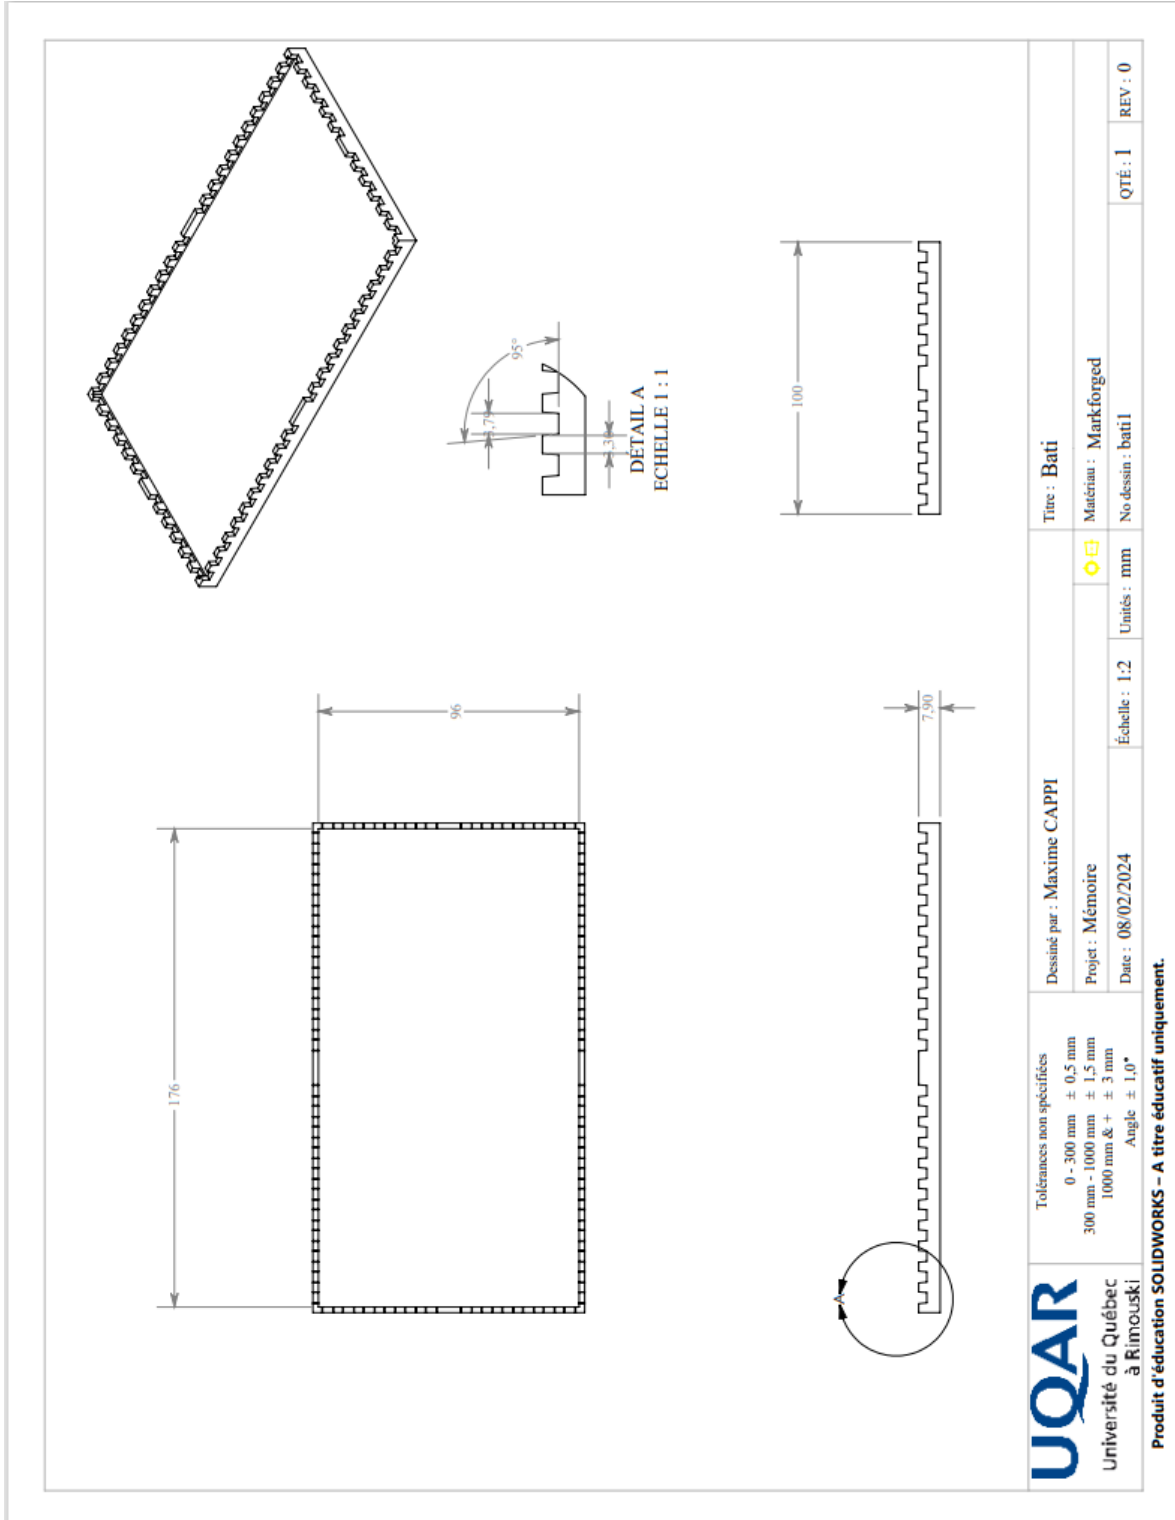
Plan de la partie inférieure du moule des éprouvettes de type I
